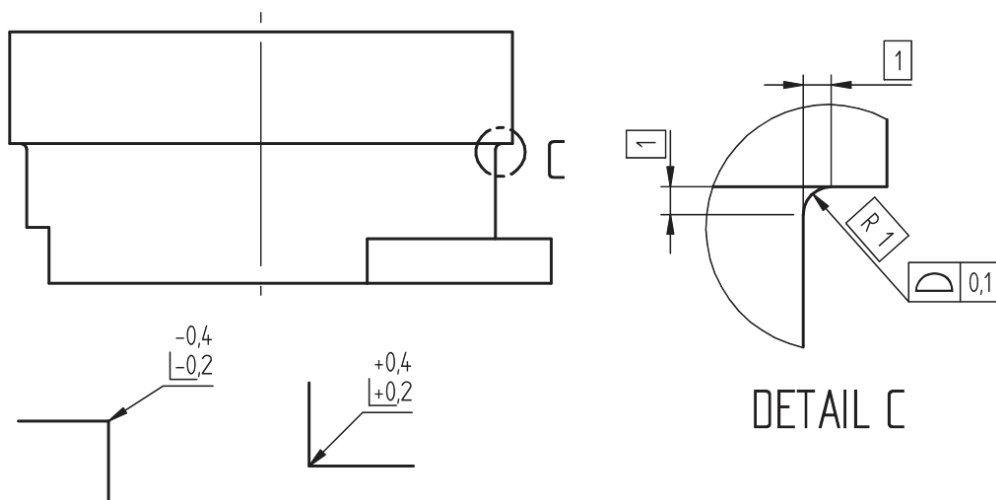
Tolerance textury povrchu pro součást "podstava"
